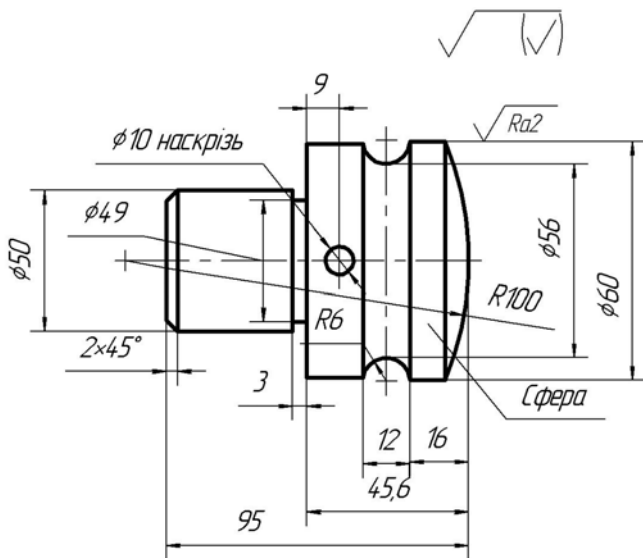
Кресленик деталі, форма якої подається у вигляді одного зображення
